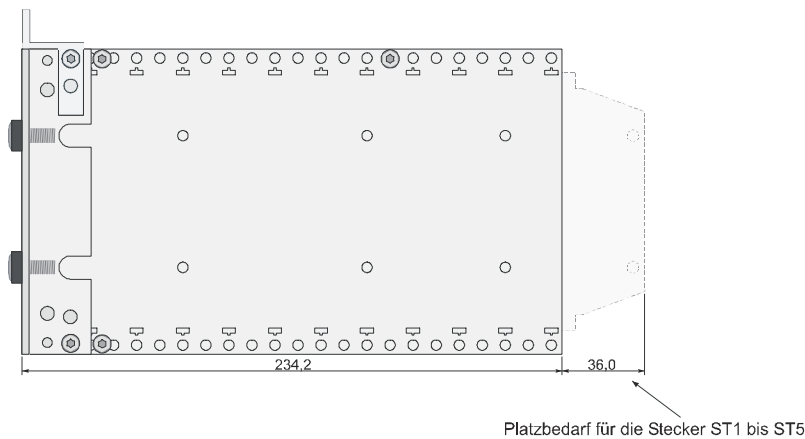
Seitenansicht des Baugruppenträgers Type BGT04 mit Beschriftungsleiste (identisch mit BGT05)
